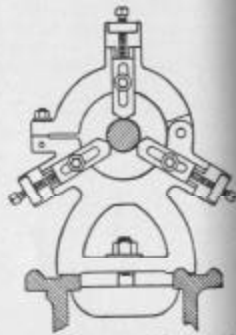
Lunette Fixe montée sur le Banc du Tour
